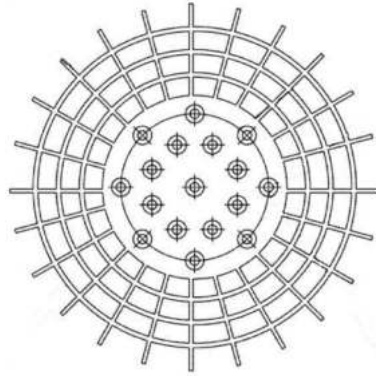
Багатоструминна головки розподільника згідно з пат. № CN103949080А
